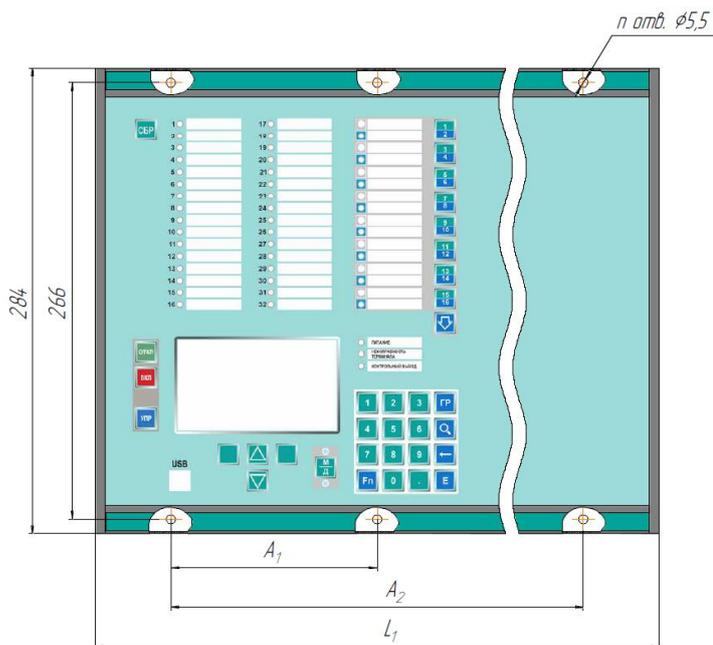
Габаритные и установочные размеры терминала БЭ2704 096/097 (вид спереди)
